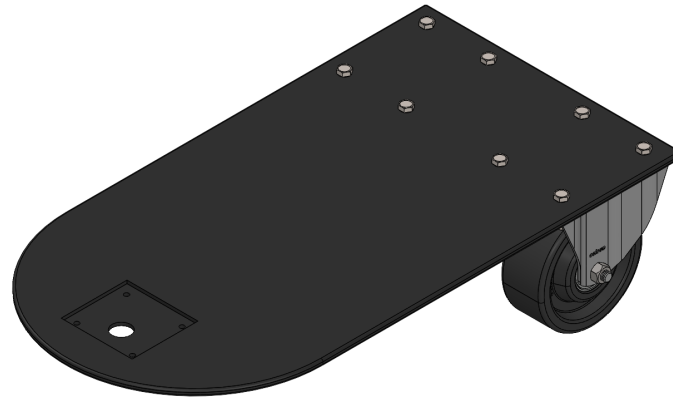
Sous-ensemble châssis de la plateforme mobile
